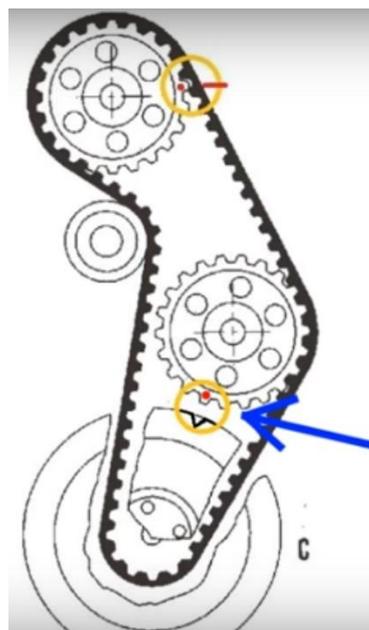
Engranaje del salto de chispa Fuente: www.todomotores.cl
